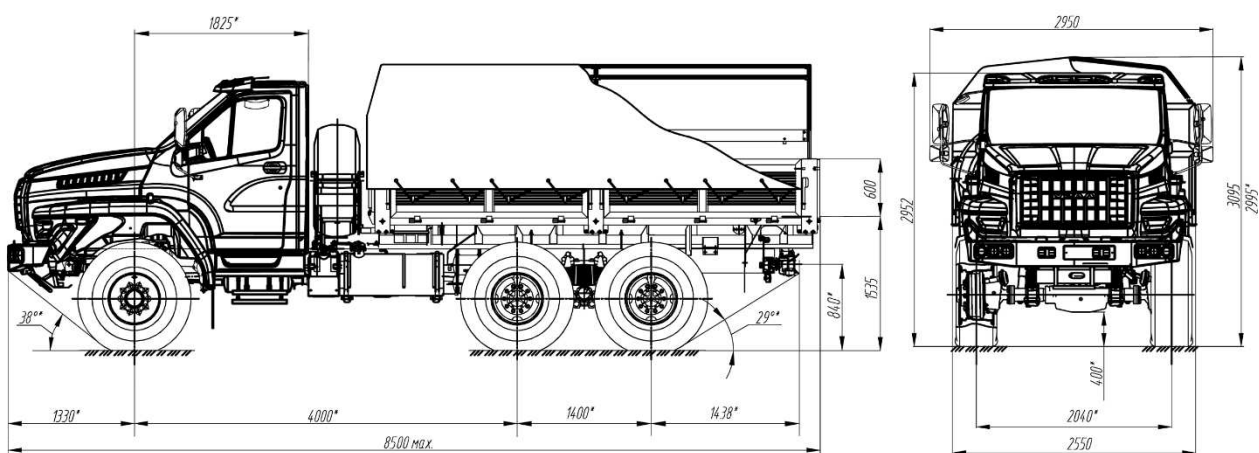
Габаритные размеры автомобиля Урал-4320-5111-73/75
